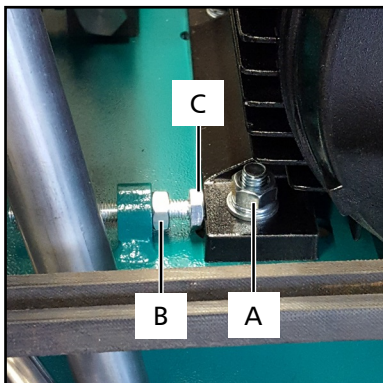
Befestigungsmutter (A) (4x), Kontermutter (B), Spansschraube (C)
